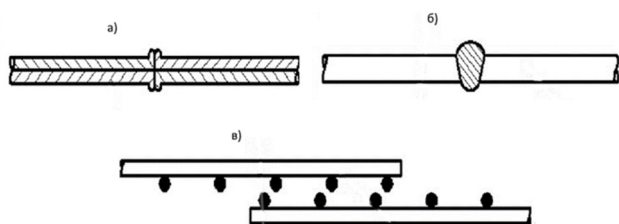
Типы креплений при дуговой сварке
